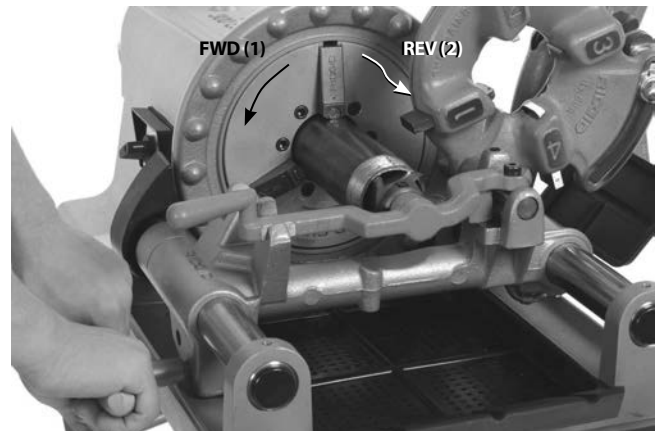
Fräsen des Rohrs mit dem Innenrohrfräser, Maschinenrotation
